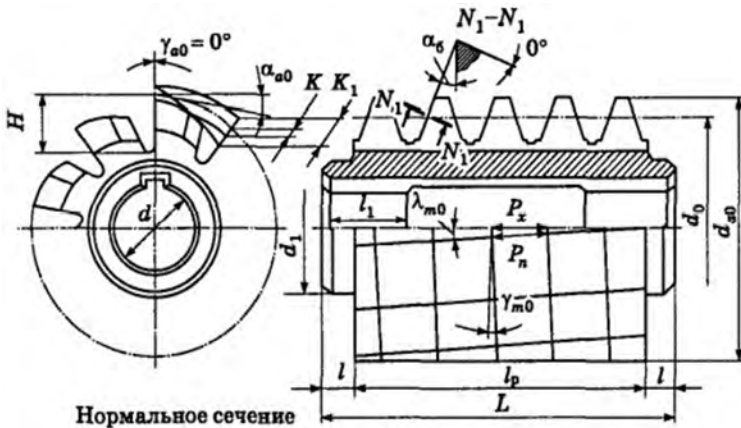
Основные конструктивные параметры червячных зуборезных фрез: L – общая длина фрезы; l_p – рабочая длина; l – длина посадочных поясков; l – длина контрольных буртиков; d_{a0} – наружный диаметр фрезы; d_o – делительный диаметр фрезы; d_1 – диаметр контрольных буртиков; d – внутренний диаметр фрезы; H – полная глубина стружечной канавки; γ_{m0} – угол наклона витков фрезы; λ_{m0} – угол наклона стружечных канавок; γ_{a0} – передний угол заточки фрезы; α_{a0} – задний угол заточки фрезы на вершине зуба; α_6 – боковой нормальный задний угол заточки фрезы; K – величина затылования (подъем кулачка затылования); K_1 – величина второго затылования
